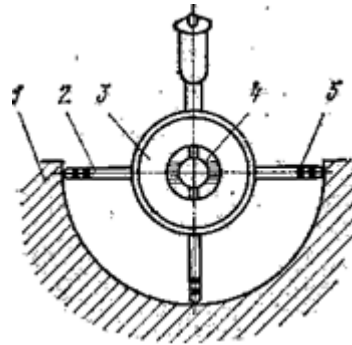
Центрошукач: 1 – розточування, 2 – вимірювальна ніжка, 3 – корпус, 4 – марка, 5 – подовжувач.
